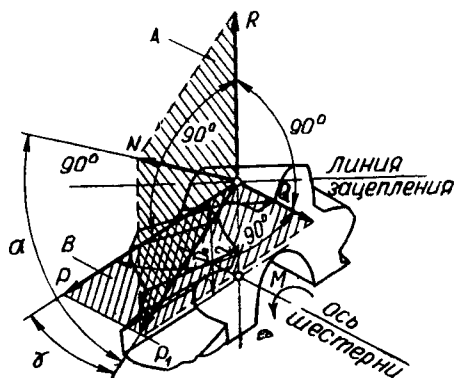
Схема цилиндрической шестерни с прямыми зубьями и сил, действующих на зубья.
